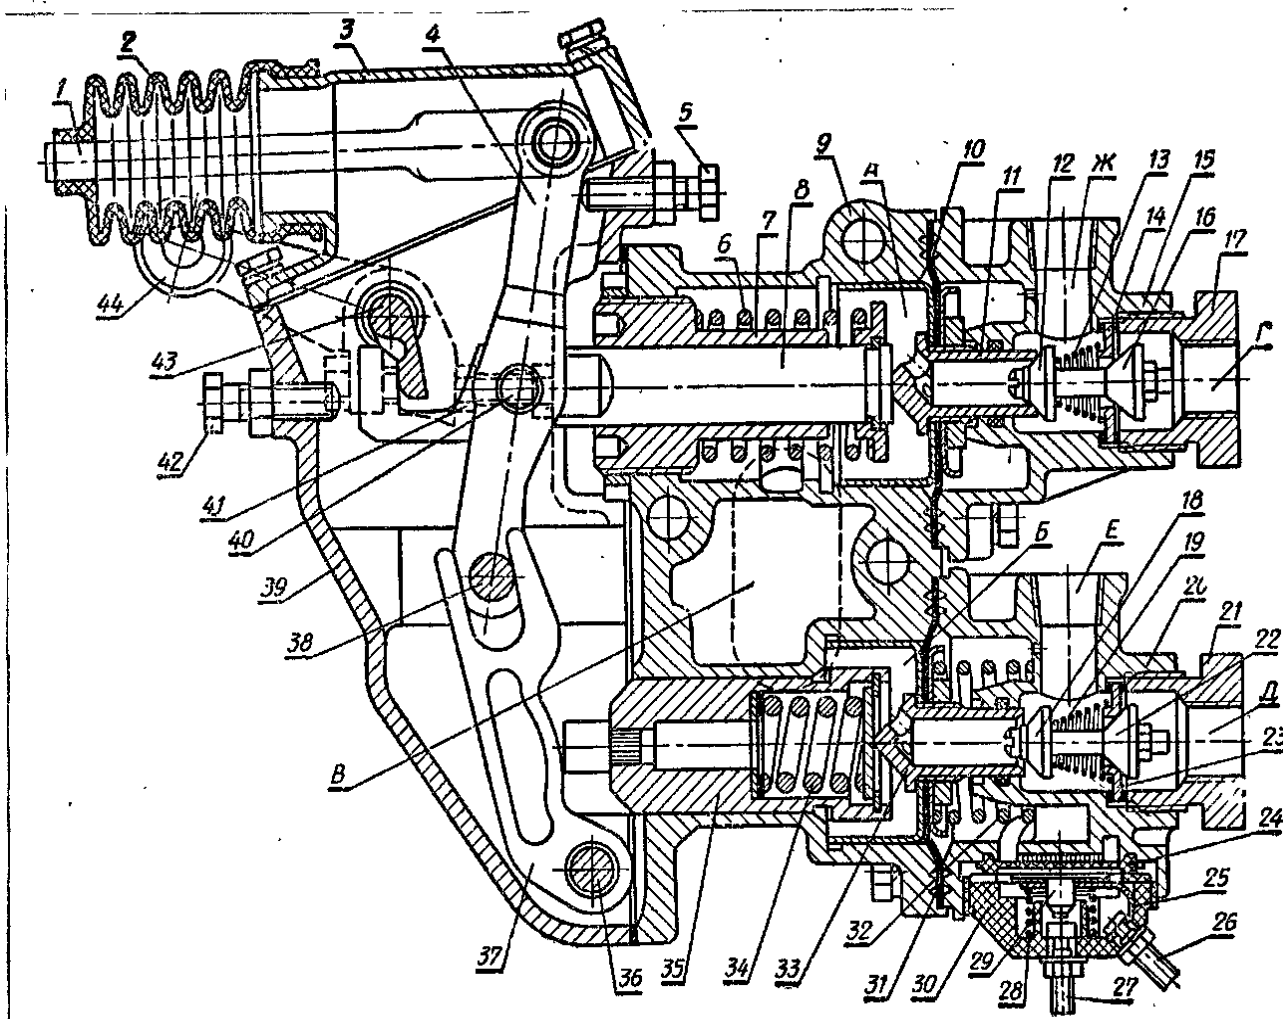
Тормозной кран: 1 – тяга; 2 – чехол; 3 – крышка корпуса рычагов; 4 – двуплечий рычаг; 5, 41 и 42 – регулировочные болты; 6 и 34 – уравнивающие пружины; 7 – направляющая пружина; 8 – шток; 9 – корпус; 10 и 31 – диафрагмы; 11 и 33 – седла выпускных клапанов; 12 и 18 – выпускные клапаны; 13 и 19 – пружины выпускных клапанов; 14 и 23 – седла впускных клапанов; 15 и 20 – крышки; 16 и 22 – впускные клапаны; 17 и 21 – штуцера; 24 – диафрагма включателя "стоп"; 25 – шинка; 28 и 27 – контакты включателя; 28 – пружина включателя; 29 – подвижной контакт; 30 – изоляционная крышка; 32 – пружина диафрагмы; 35 – стакан; 36, 33 и 40 – оси; 37 – малый рычаг; 39 – корпус рычагов; 43 – валик; 44 – рычаг наружный; А и Б – полости перед диафрагмами; В – выпускное окно; Г, Д – полости над впускными клапанами; Е, Ж – полости над выпускными клапанами.
